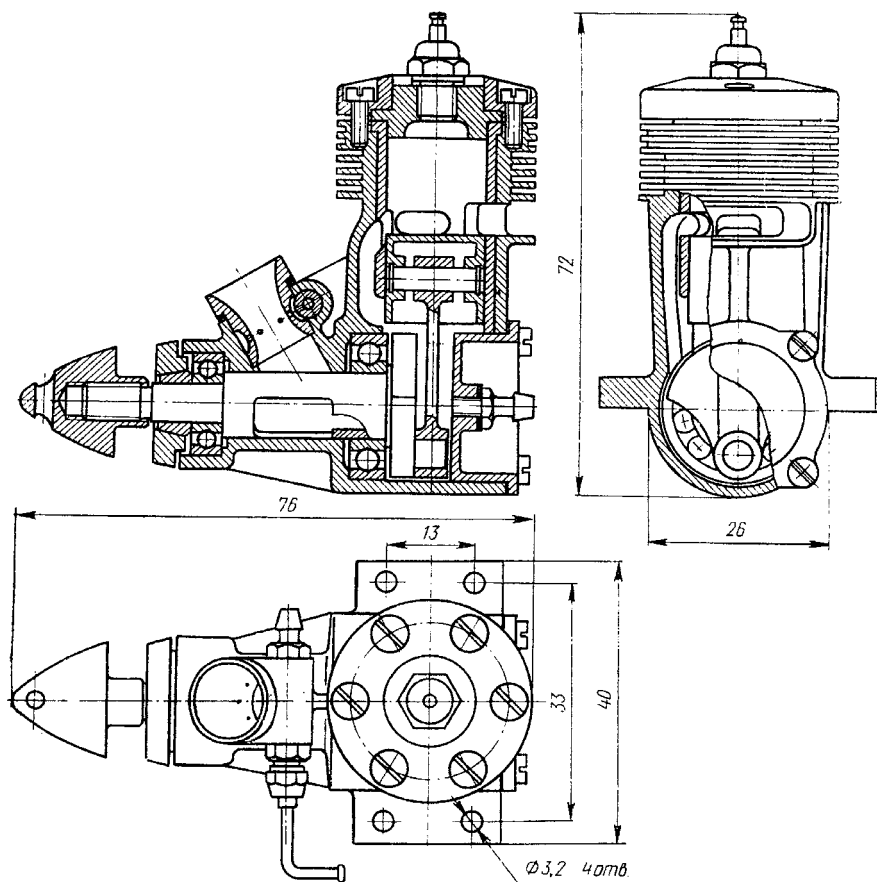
Двигатель ЦСТКАМ-2,5 К
